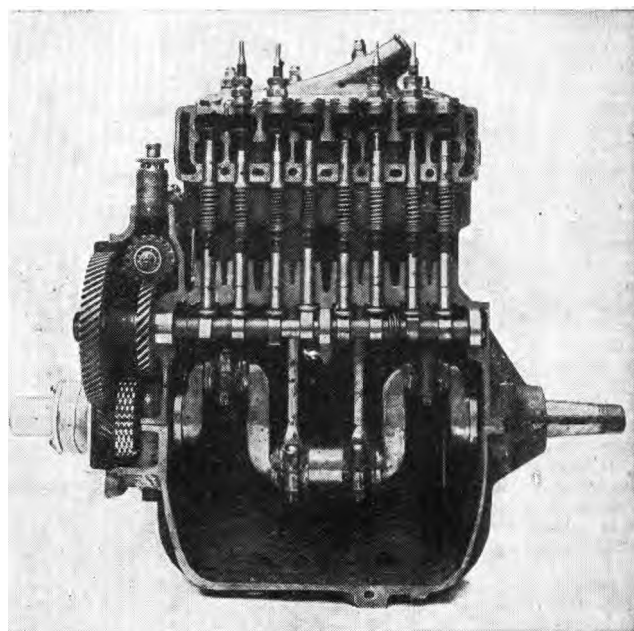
Coupe transversale d'un moteur vertical à 4 cylindres passant par l'axe des soupapes (Renault).
